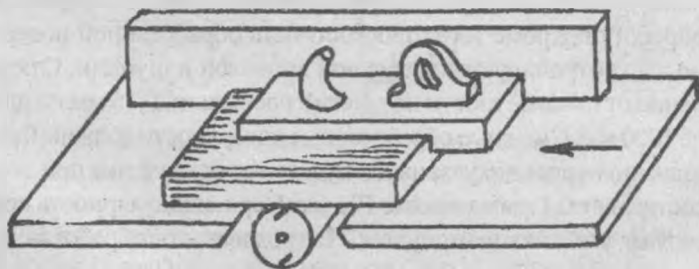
Схема обработки мелких деталей с помощью толкателя
